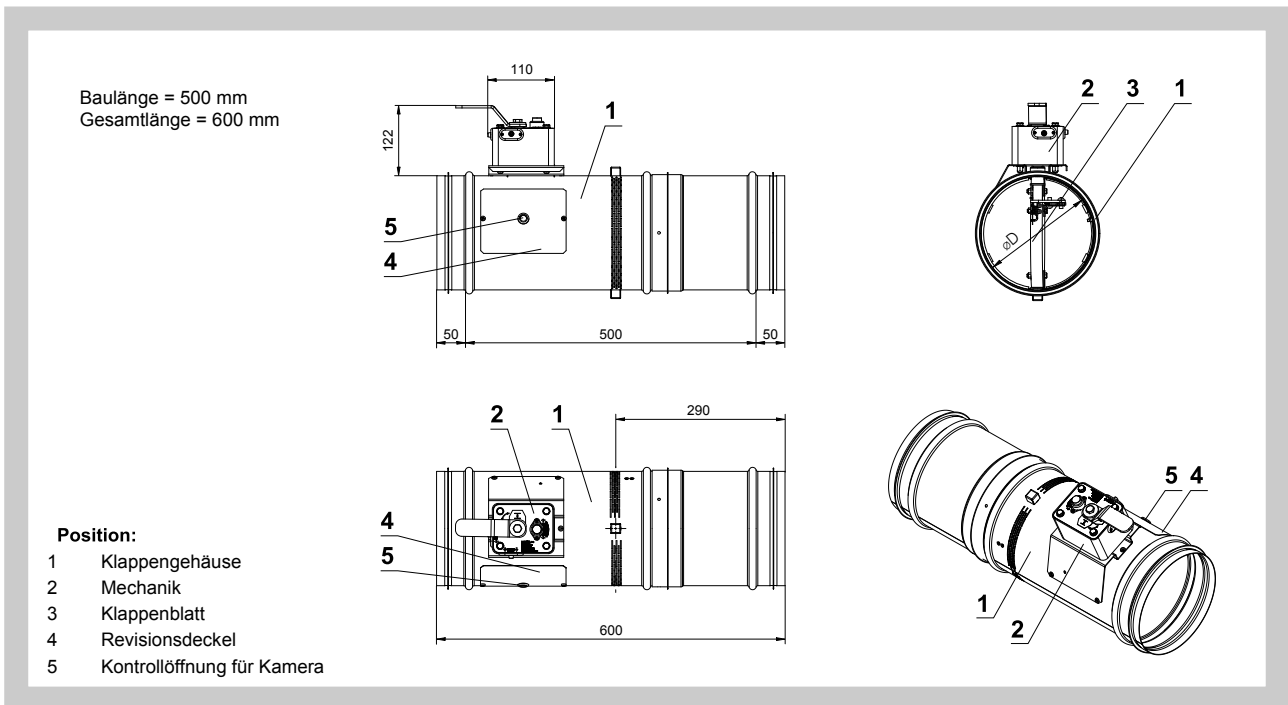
AUSFÜHRUNG MIT STELLANTRIEB
